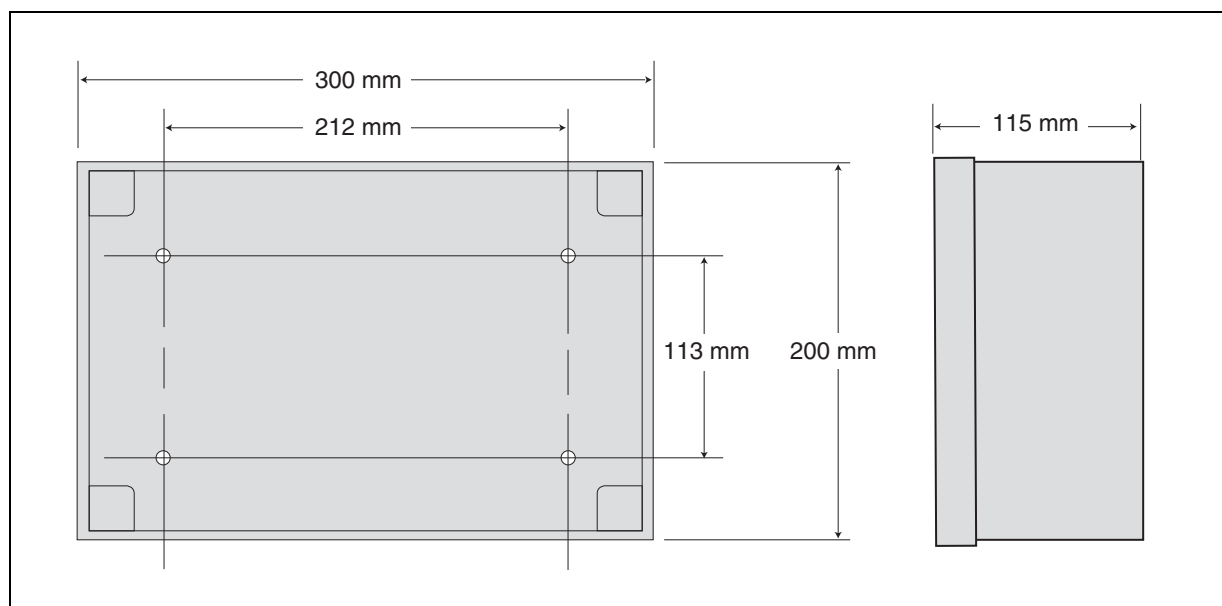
Caixa do terminal TLS - Dimensões totais e de fixação
